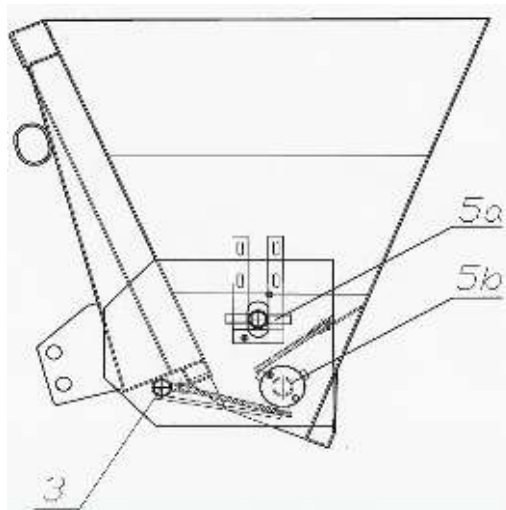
hoved seksjonen: 3 - utlading regulator, 5a - strimling aksel, 5b - mater akselen.
